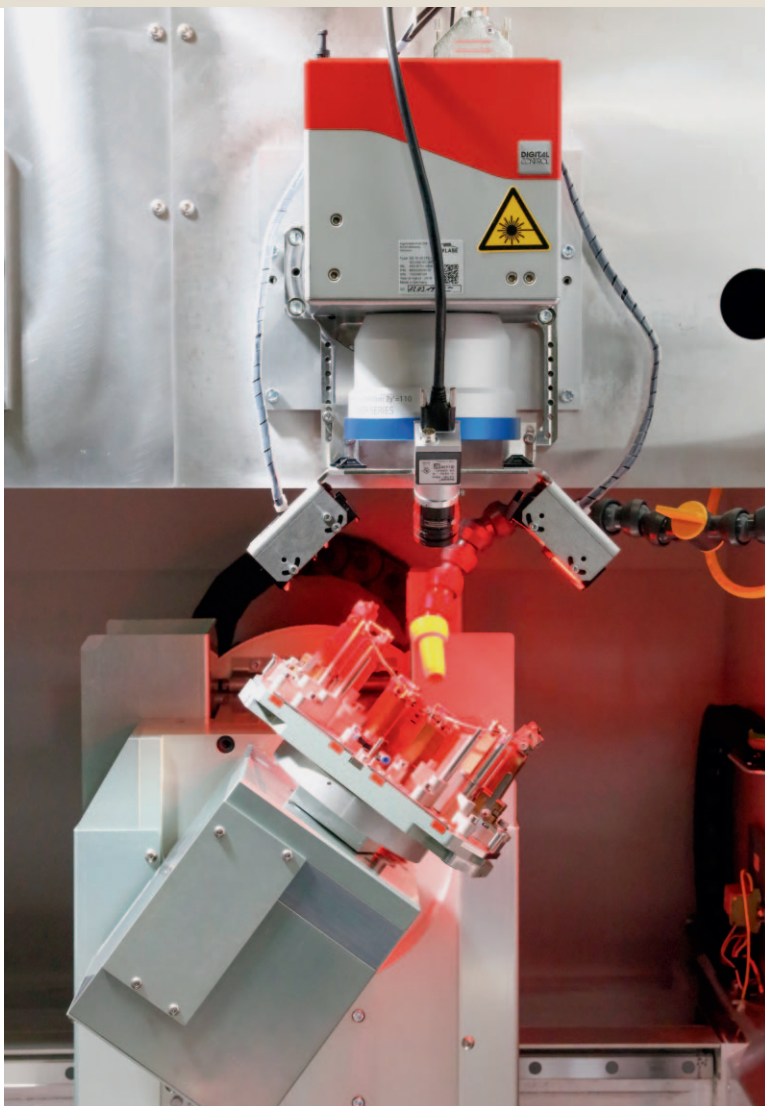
3D-Laserschweißen mittels künstlicher Intelligenz
